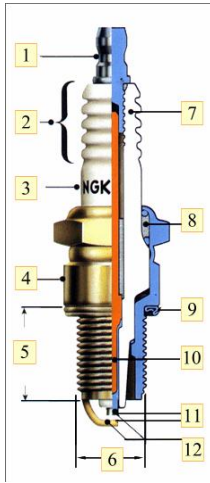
Устрій свічки запалювання з плоскою опорною поверхнею: 1 - контактна (штекерна) гайка; 2 - оребрення ізолятора (бар'єри струму); 3 – керамічний ізолятор; 4 – корпус свічки; 5 – різьбова частина корпусу; 6 – діаметр різьбової частини; 7 – керамічний ізолятор; 8 – температуростійкий ущільнювач; 9 – ущільнююче кільце; 10 - контактний стержень (центральный електрод з струмопровідним герметиком); 11 - іскровий зазор; 12 – боковий електрод ("маси").
